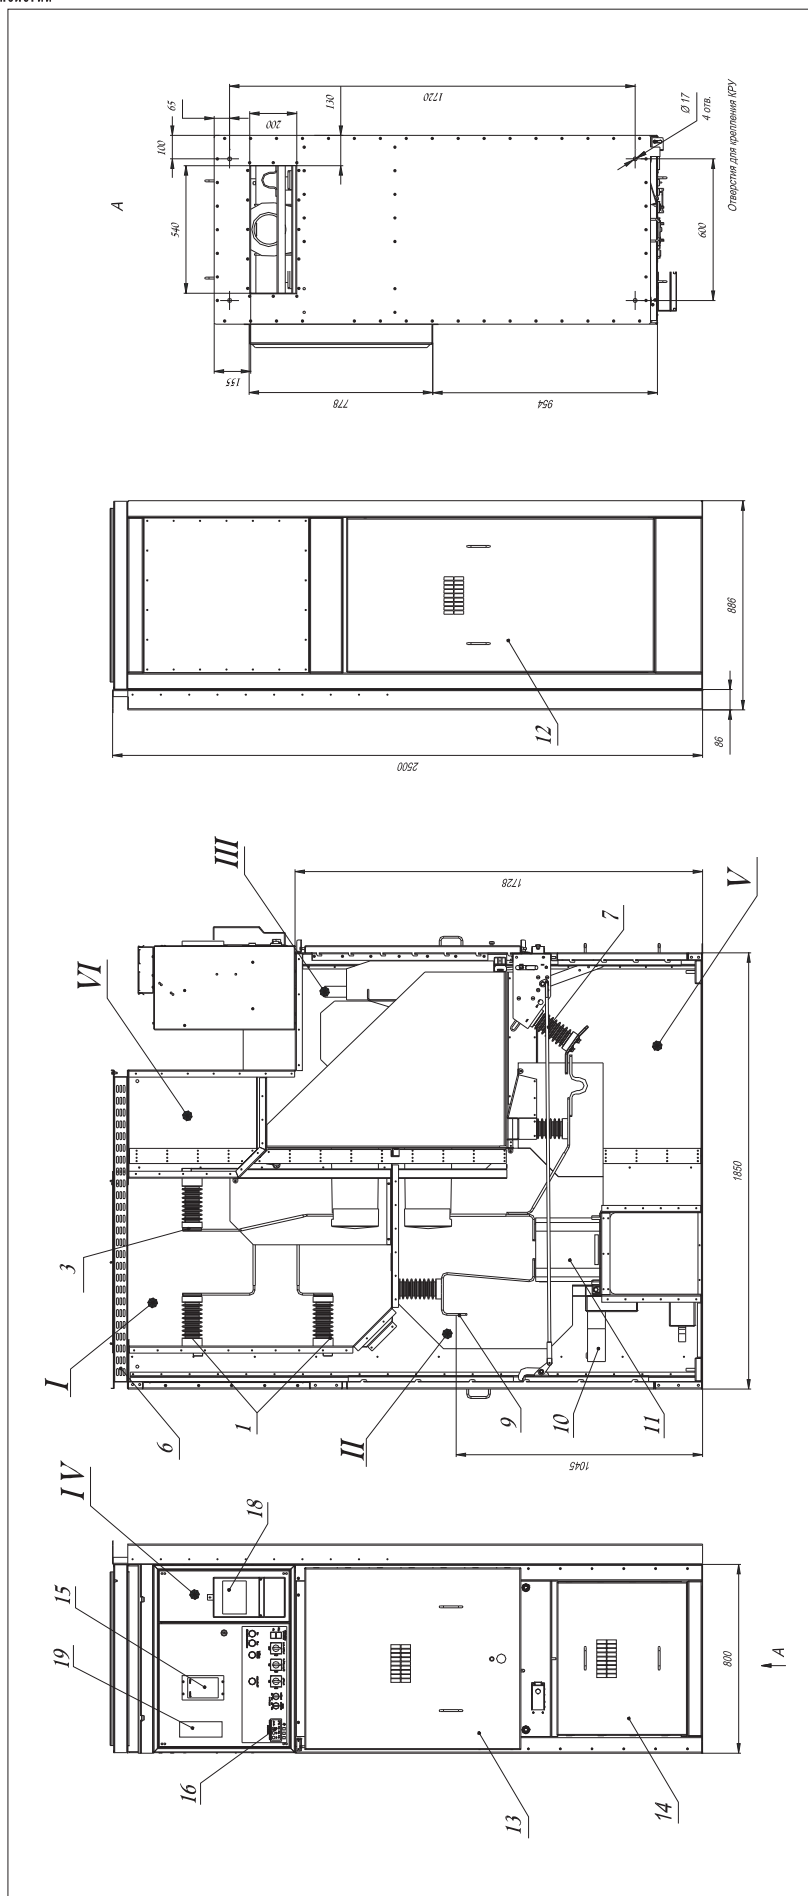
Общий вид и габаритные размеры КРУ2-СТ20
